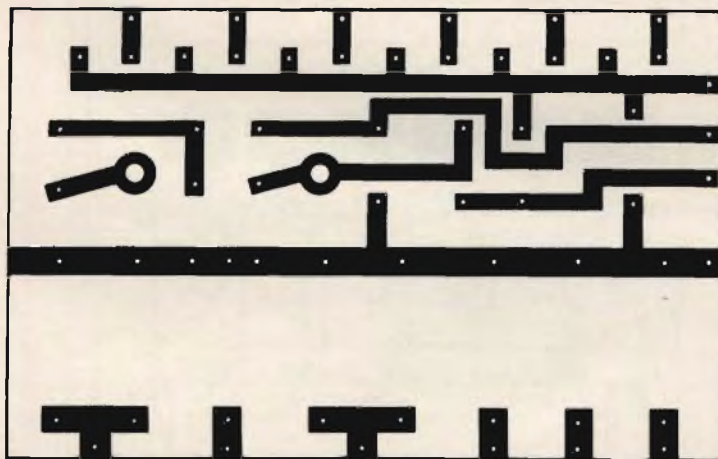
Circuito stampato visto dal lato delle saldature.
